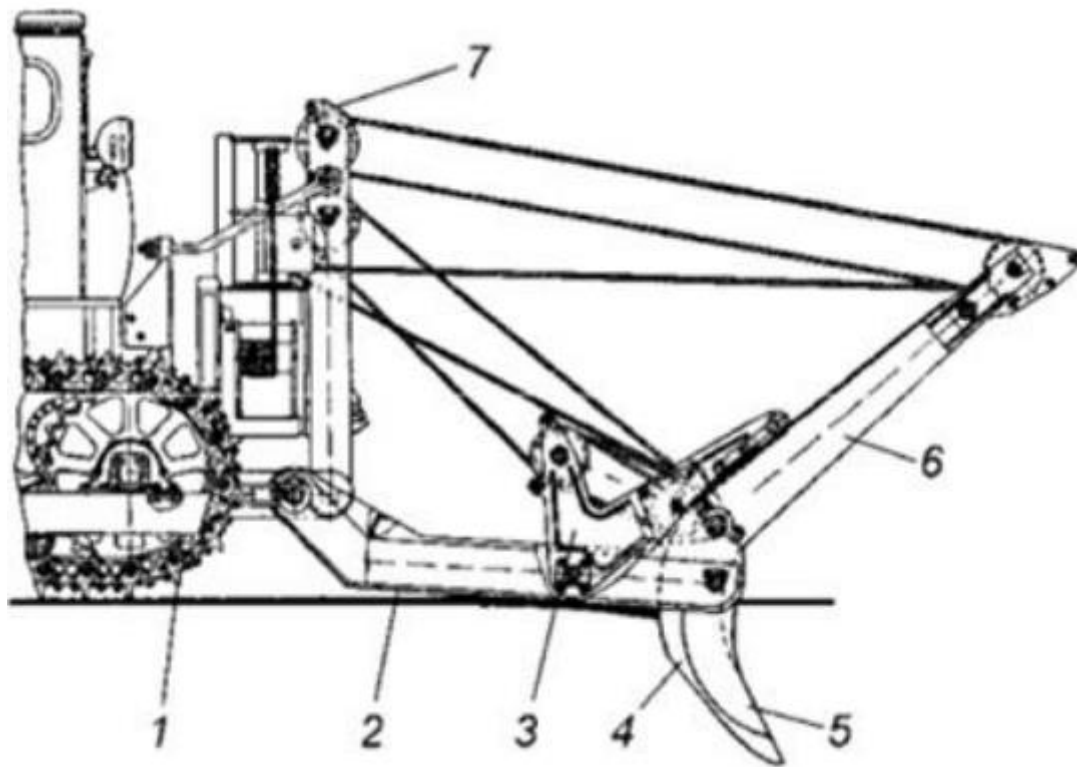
1-базовый трактор; 2- рама; 3- малый рычаг; 4- зуб корчующего рычага; 5- клык-собираетель; 6- корчующий рычаг; 7- полиспаст привода корчующего оборудования
